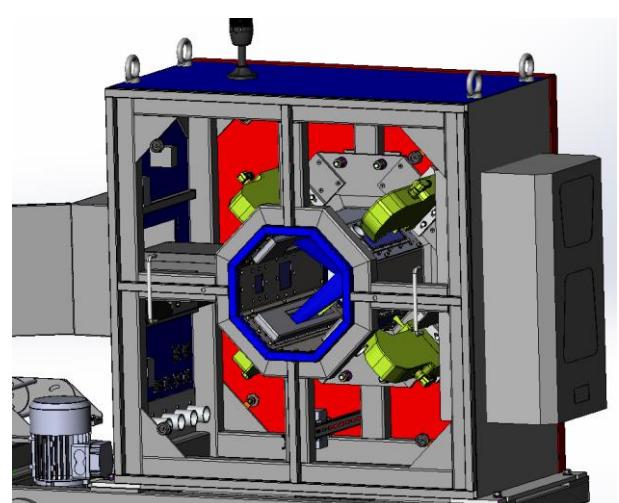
Общий вид портала измерительного с лазерными 2D-профилометрами
